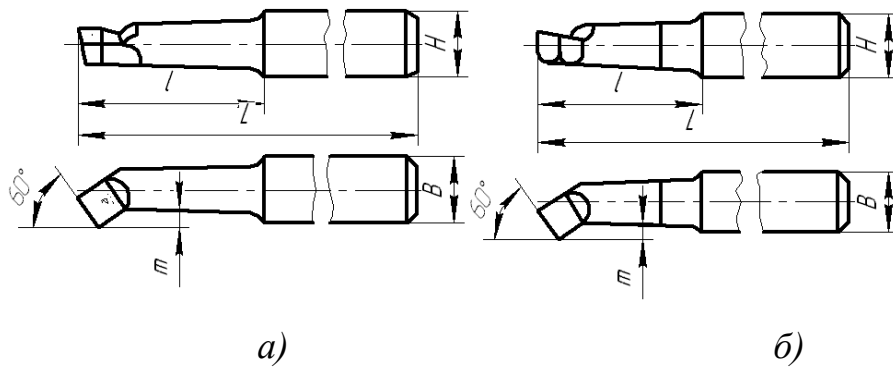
Різці розточувальні для оброблення наскрізних отворів:
